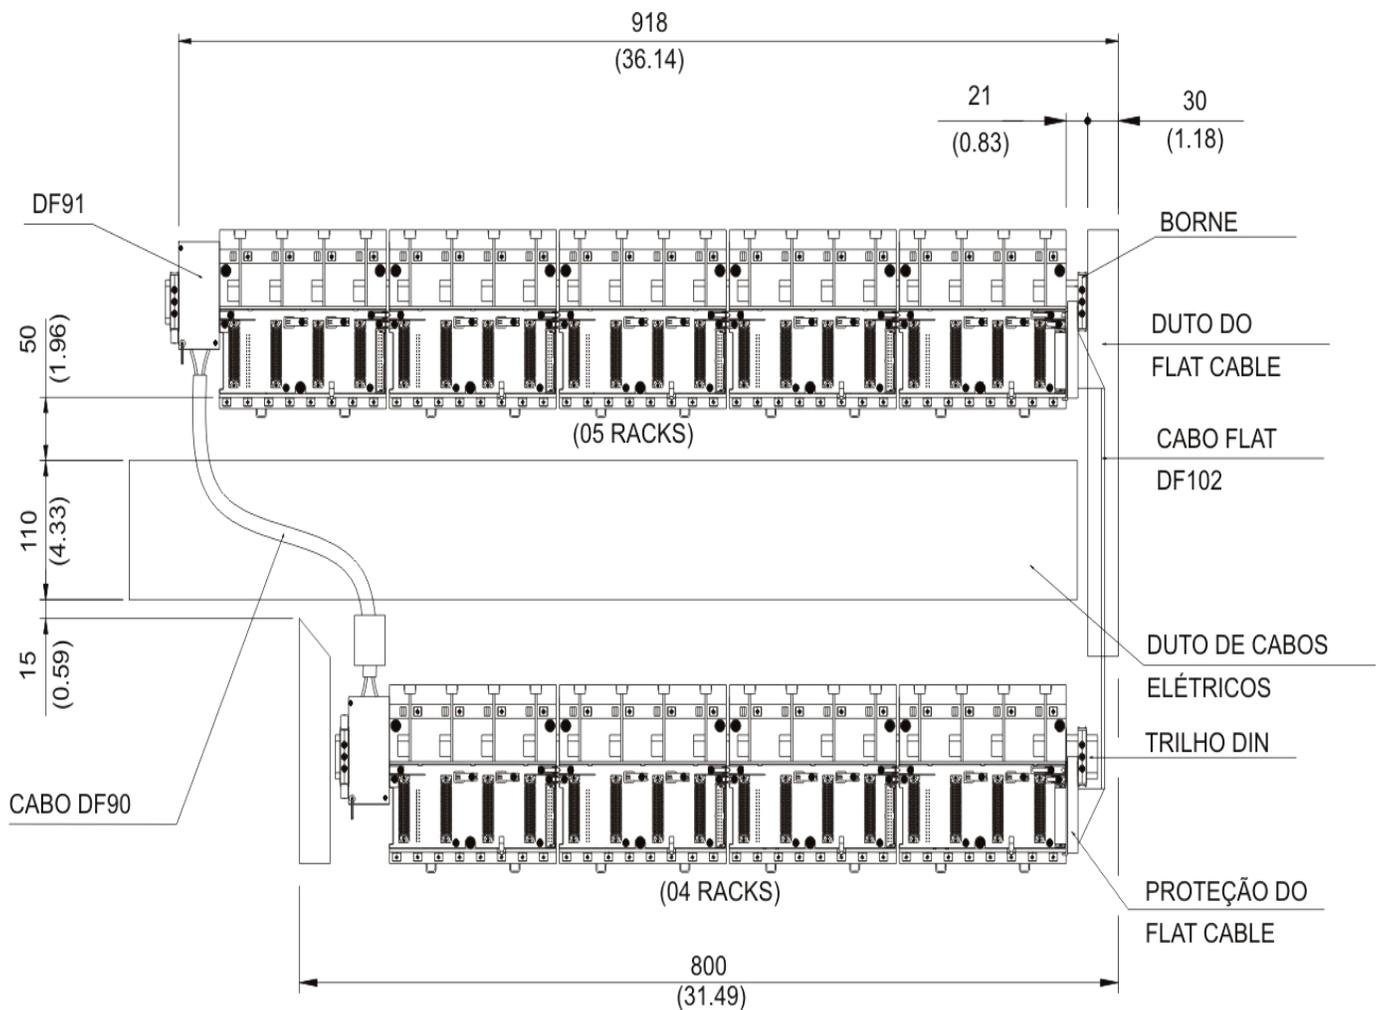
Desenho Dimensional dos Racks e Módulos
